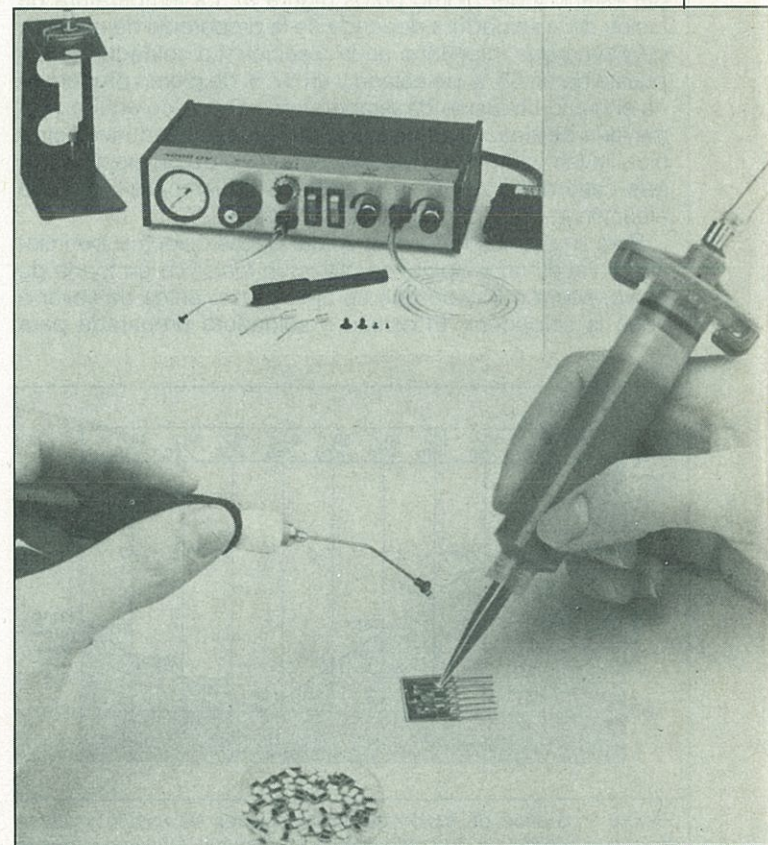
Aparato preparado para dosificar soldadura y manipular componentes diminutos.
